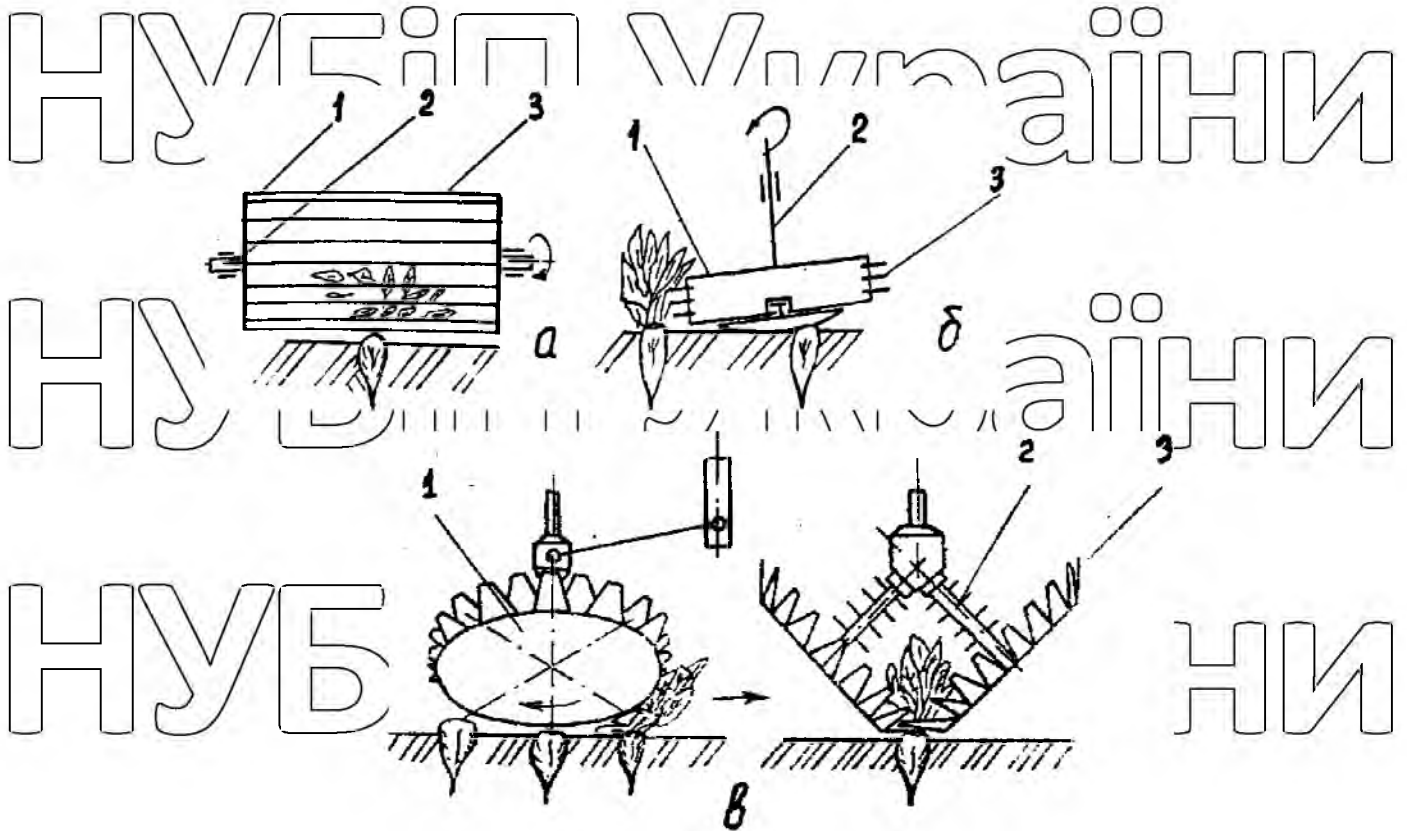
Гичкорізальні апарати, що поєднують процес копіювання й зрізу: 1 - диск; 2 - вал; 3 - ніж; а - барабан зі сталевими сегментами; б - ротор із шарнірно укріпленими ножами; в - два похило встановлені диски з ножами
